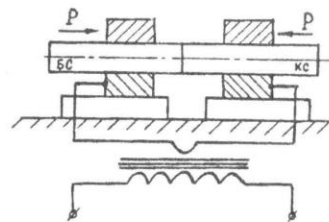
Схема электрической стыковой сварки заготовок
